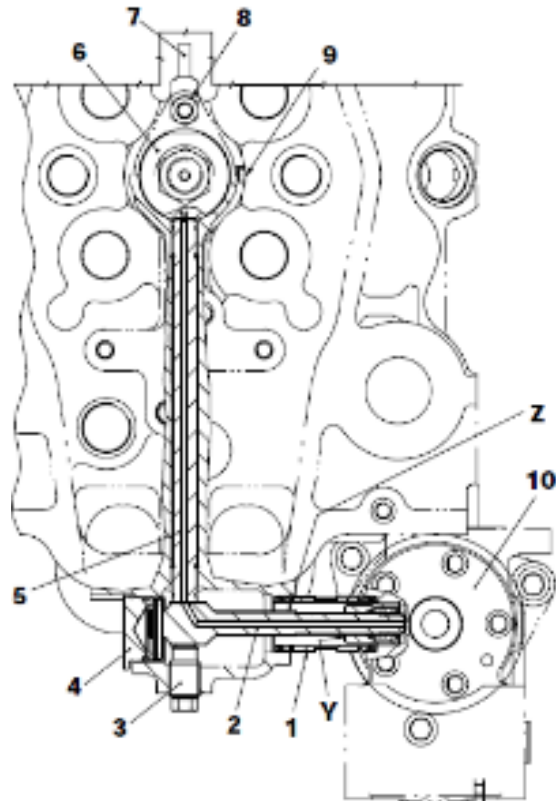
Sistema desde la bomba de inyección hasta el inyector
